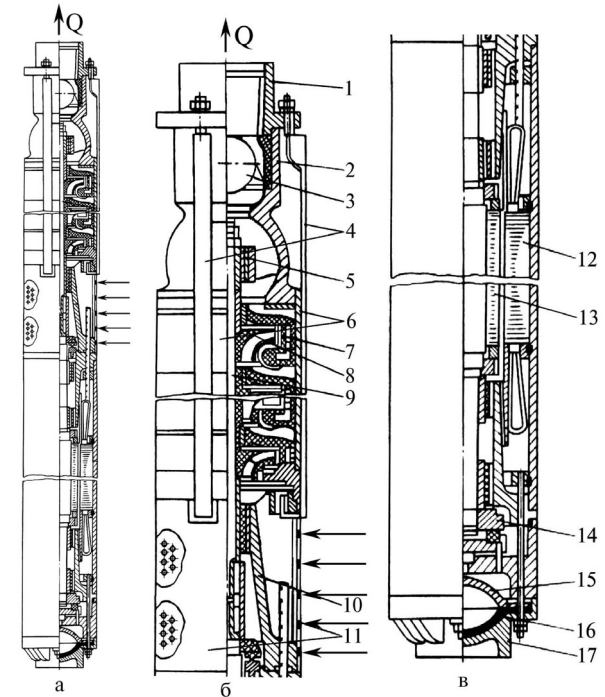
Занурювальний відцентровий насос ЕВВ: а - загальний вигляд; б - насос; в - електродвигун; 1 - напірний патрубок; 2 - корпус радіального підшипника; 3 - шаровий зворотний клапан; 4 - стяжка; 5 - радіальний підшипник; 6 - обойма лопатевого відводу (корпус секції); 7 - направляючий апарат; 8 - робоче колесо; 9 - вал; 10 - підвід (вхід) води; 11 - сітка; 12 - статор електродвигуна; 13 - ротор електродвигуна; 14 - радіально-упорний підшипник ковзання; 15 - обмежувач; 16 - діафрагма; 17 - днище.
